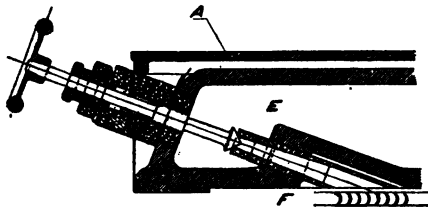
Dampfdüsen-Querschnitt einer 30pferdigen de Laval-Turbine.
